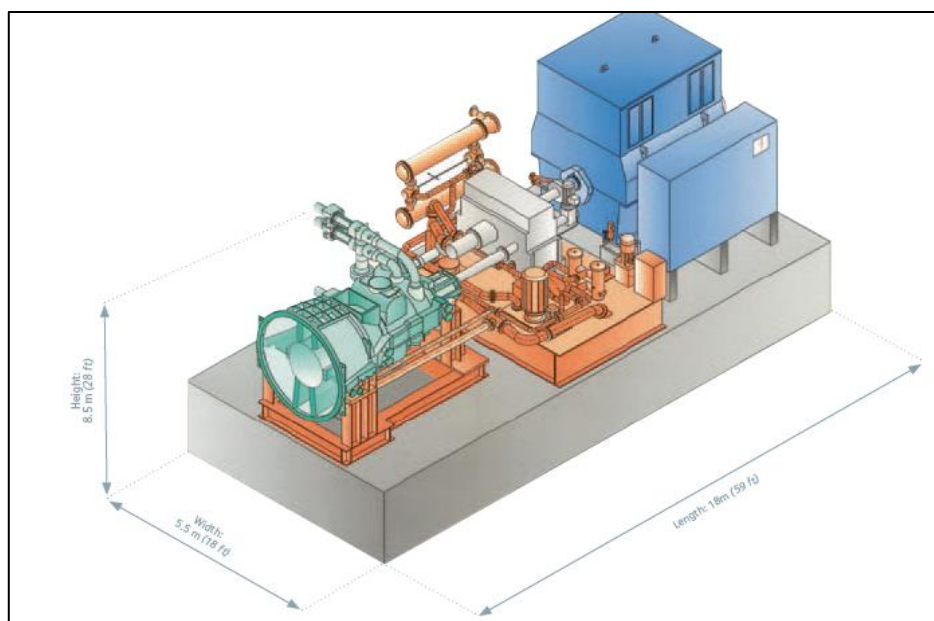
Diseño de turbina Siemens SST-400 GEO size 1.
